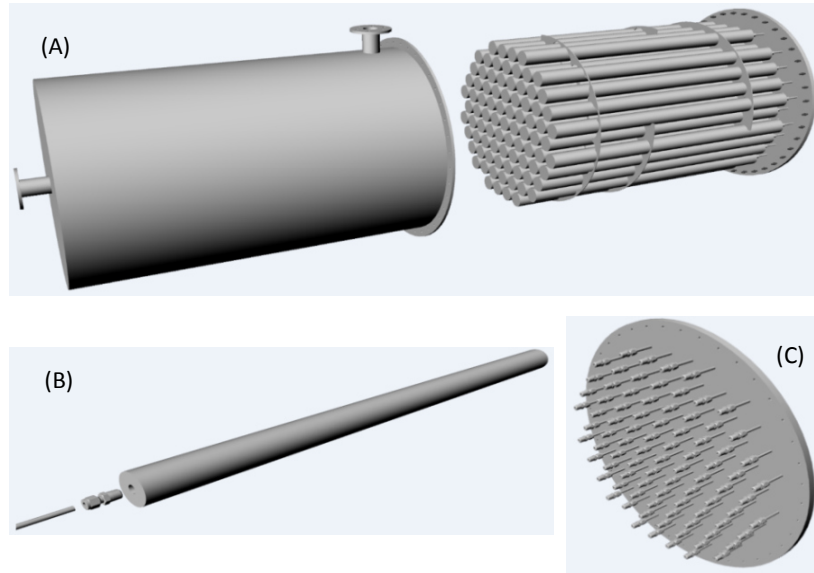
Esquema del equipo almacenador de diseño modular.
